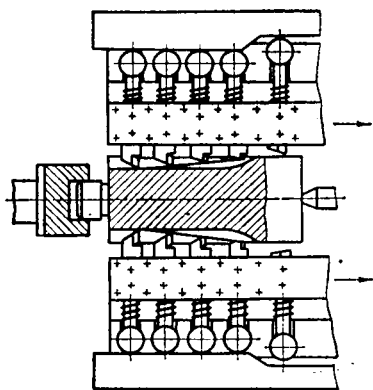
Схема протягивания шлицев вала двумя блочными протяжками
